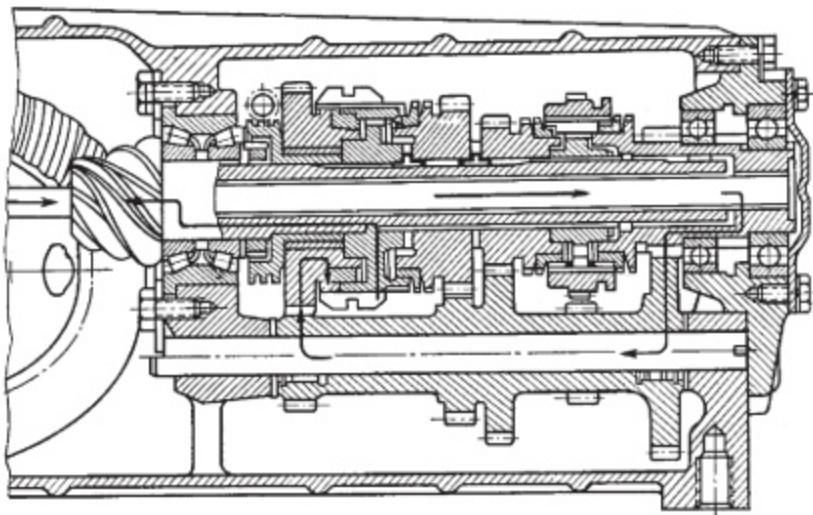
3-вальная коробка передач с коаксиальными первичным и вторичным валами
